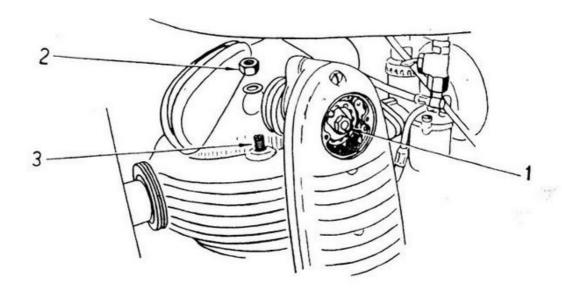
Smontaggio della testa: 1) Dado bloccaggio pignone sull'albero a camme - 2) Dadi fissaggio testa - 3) Colonnette fissaggio testa.
